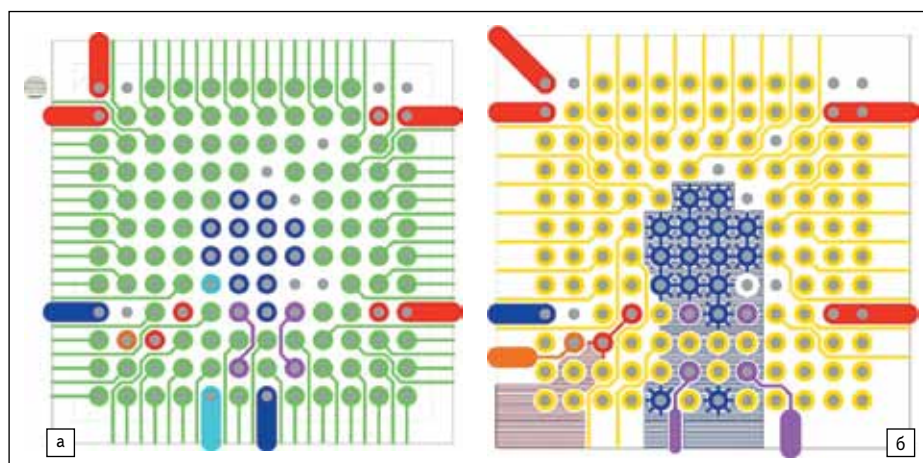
Трассировка печатной платы под корпус МК 6109.144-А: а) слой TOP; б) слой BOTTOM
